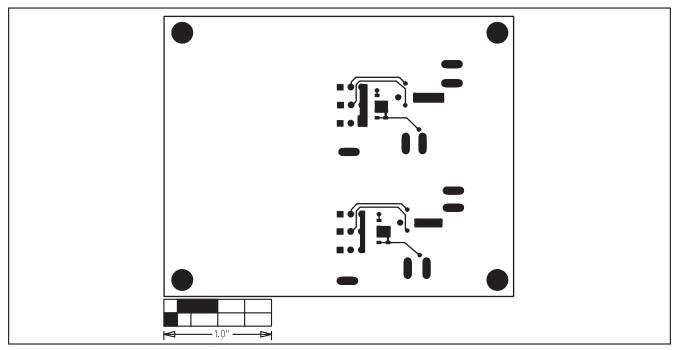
MAX1556 评估板 PCB 布局图 ___ 焊接面
